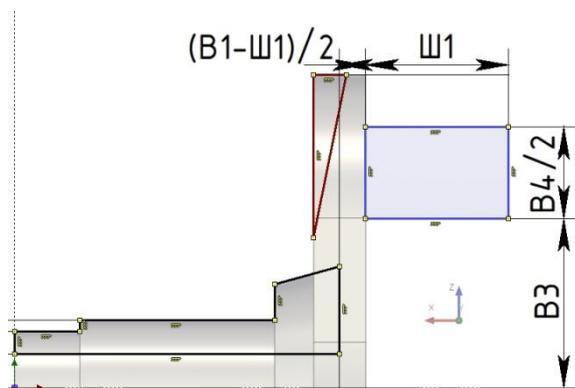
3D-профиля фаски щеки и шатунной шейки
